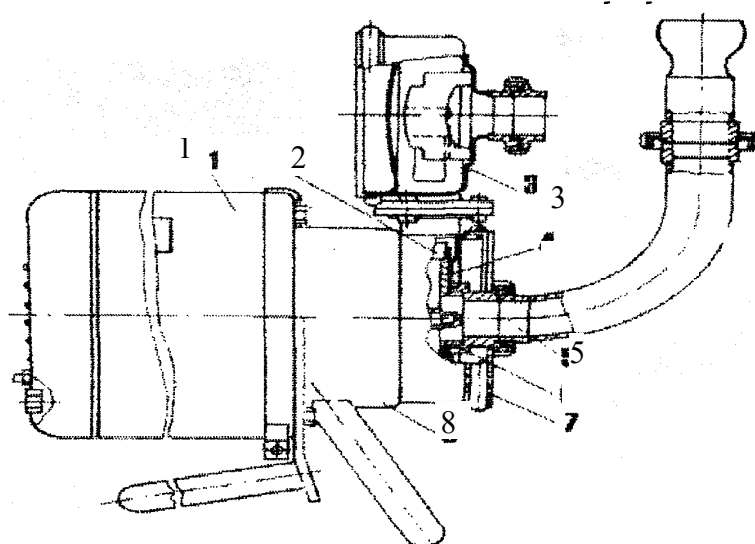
Самовсмоктуючий відцентровий насос: 1 – двигун; 2 – сопло; 3 – повітровідділювач; 4 – кришка; 5 – всмоктуючий патрубок; 6 – робоче колесо; 7 – зажимний пристрій; 8 – корпус.
